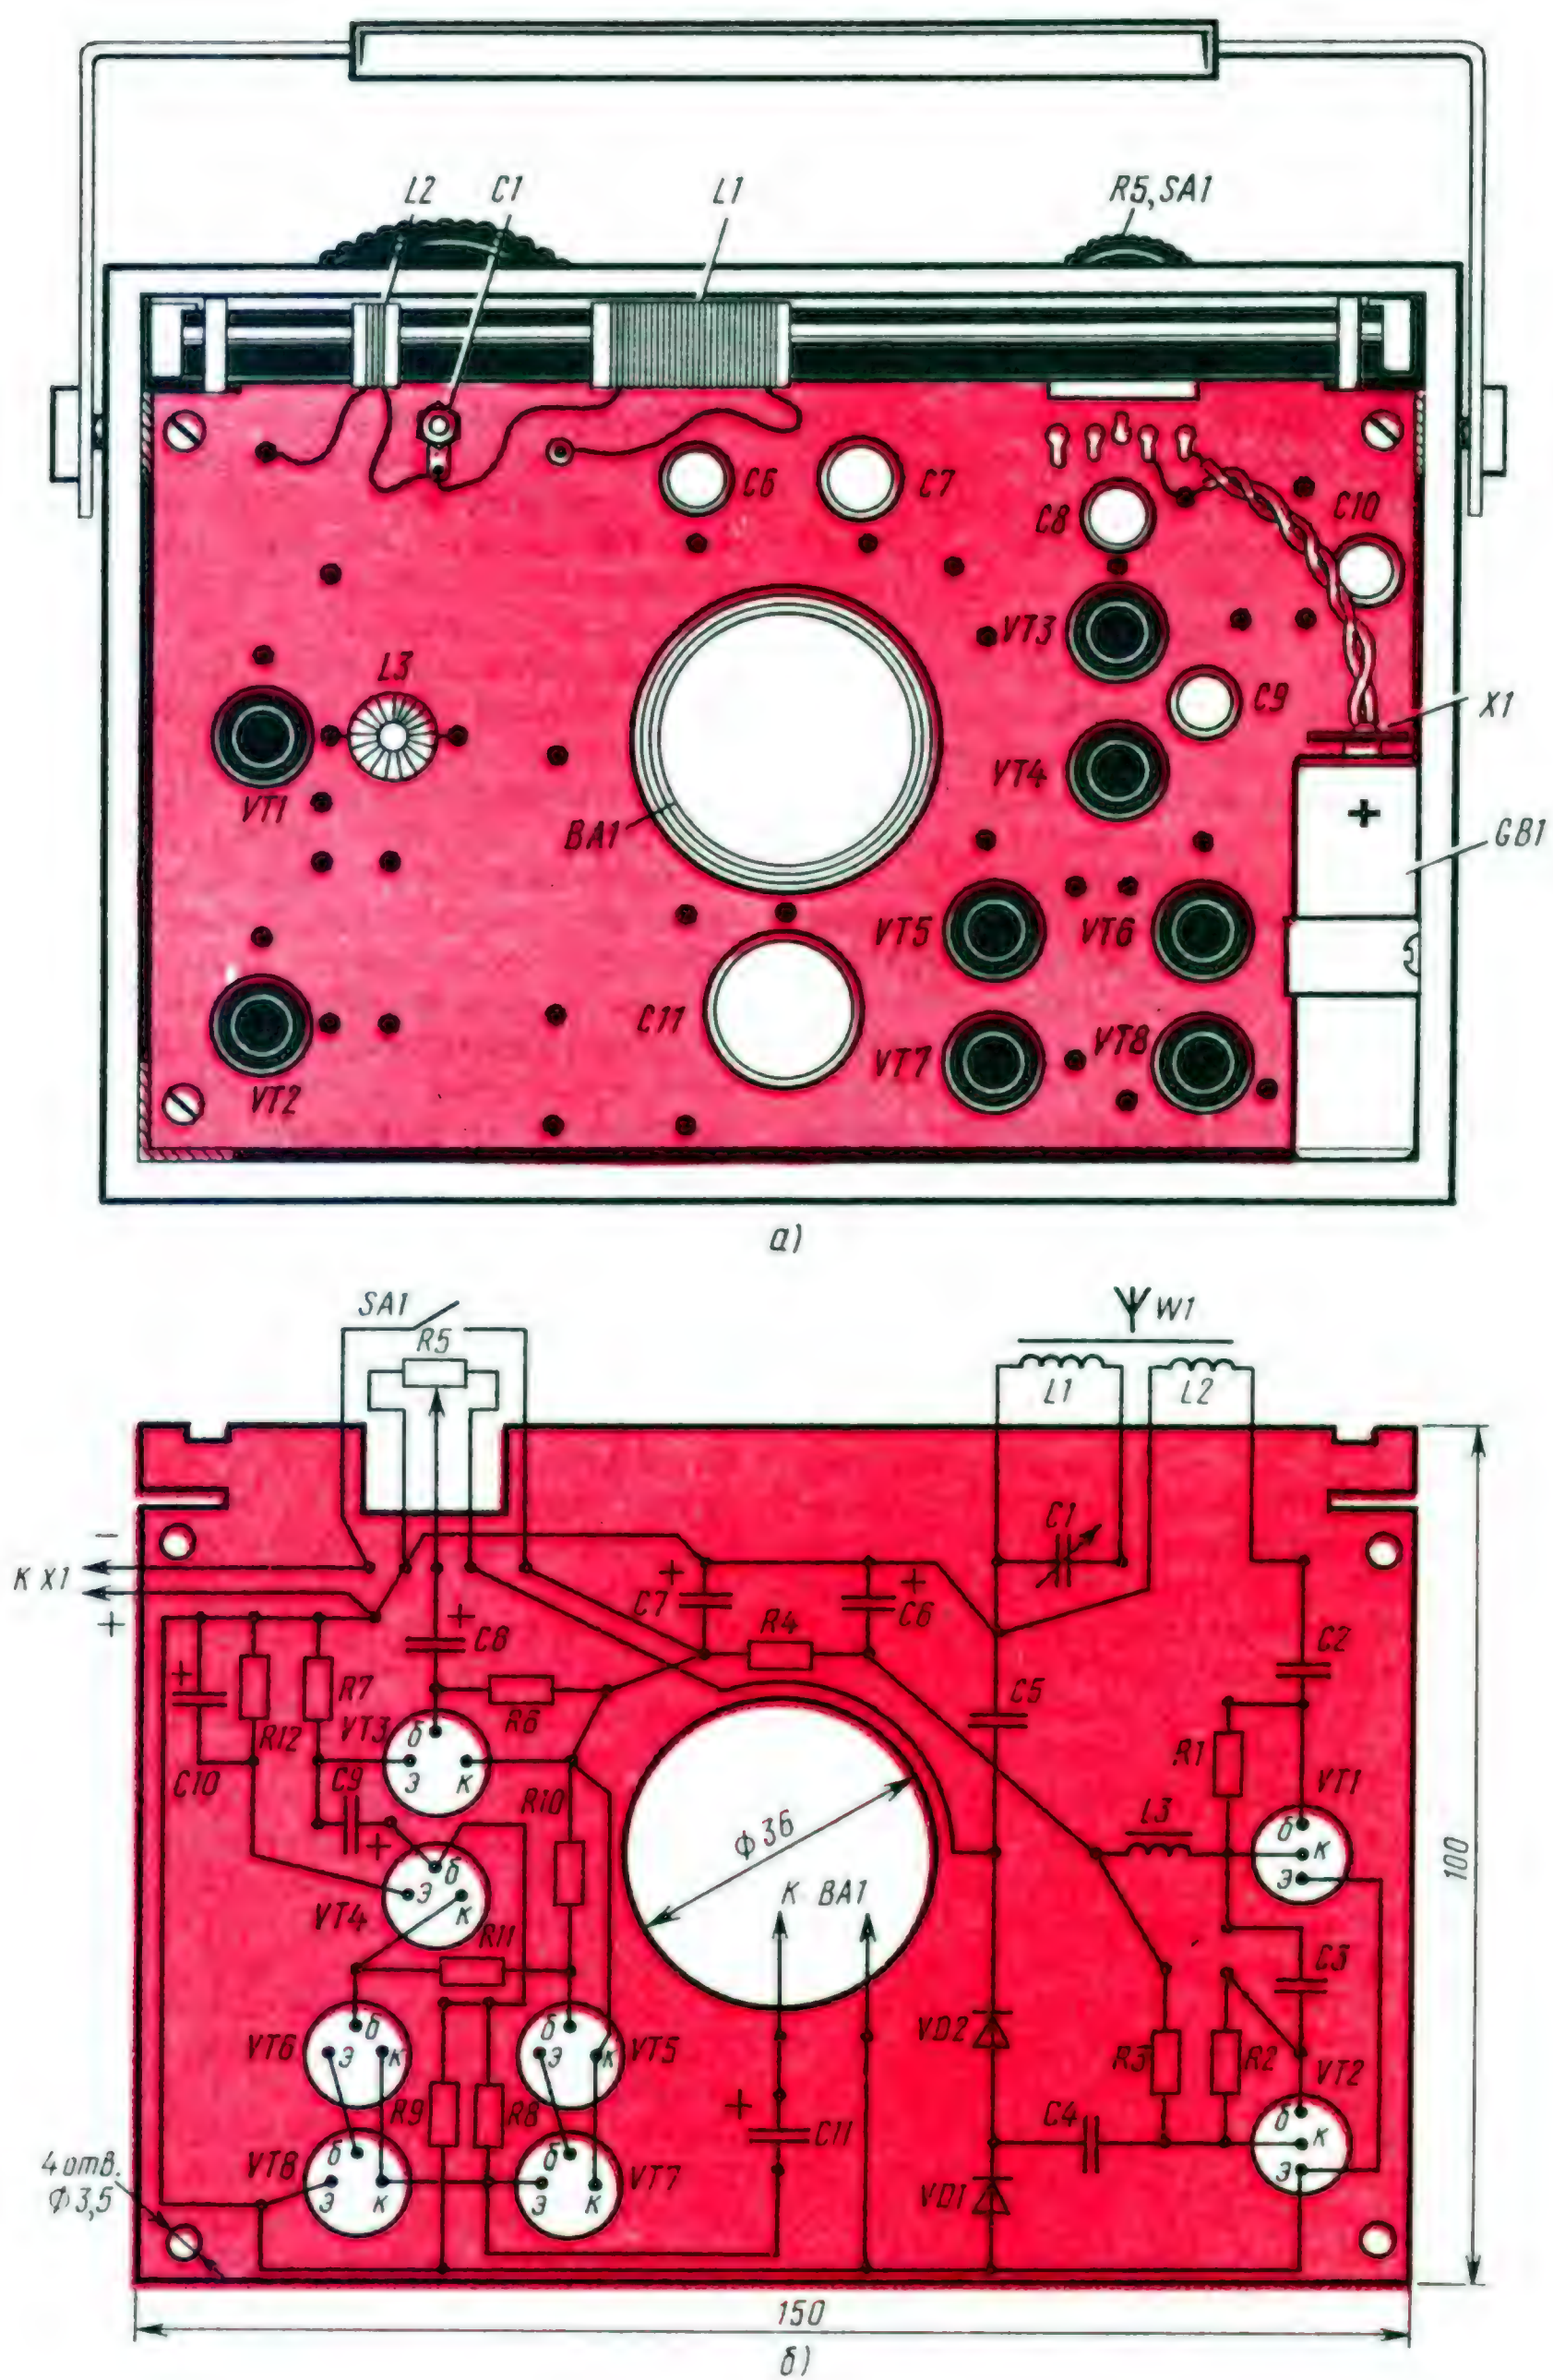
Конструкция (а) и схема размещения и соединений деталей на монтажной плате (б)
